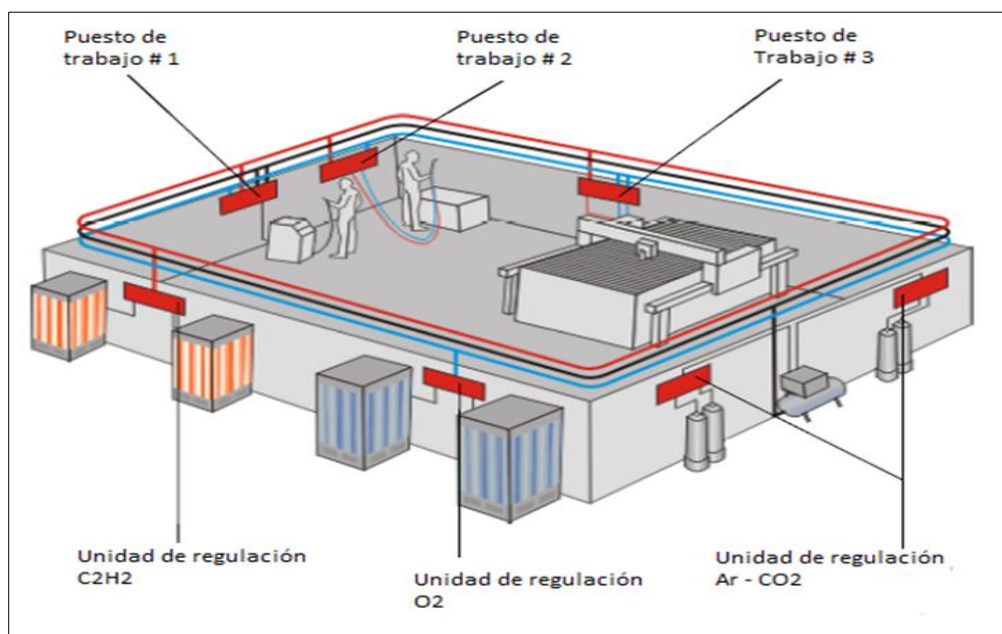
EQUIPO DE CORTE Y SOLDADURA OXI-ACETILÉNICA
